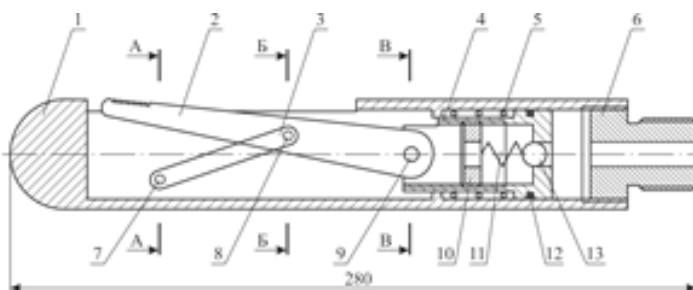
Схема щелеобразователя гидравлического по уголю (ЩГУ): 1 – корпус; 2 – режущий орган; 3 – кронштейн; 4 – поршень; 5 – пружина возврата; 6 – переходник; 7, 8, 9 – оси крепления; 10 – опорная регулирующая гайка; 11 – пружина; 12 – уплотнение; 13 – шарик
